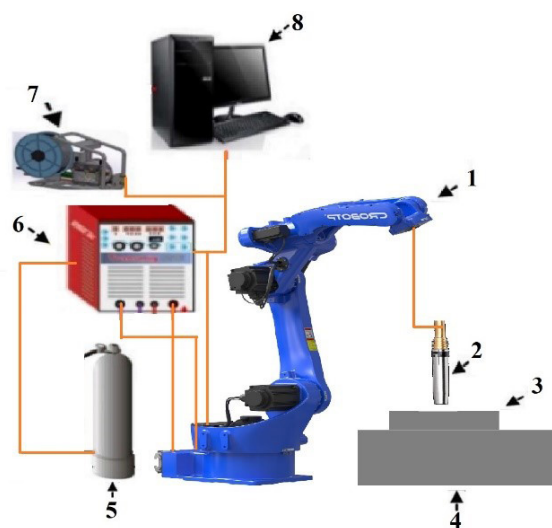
Схема комплекса для наплавки: 1 – промышленный робот; 2 – сварочная горелка; 3 – основа для наплавки; 4 – сварочный стол; 5 – баллон с защитным газом; 6 – источник питания; 7 – механизм подачи проволоки; 8 – система управления
